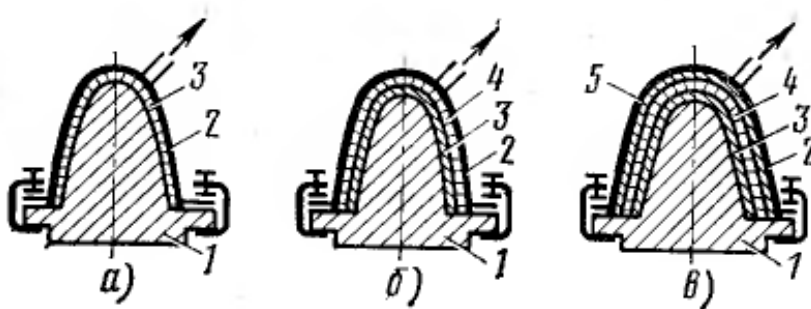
Схема виготовлення обтічника з базування по внутрішньому контуру;
